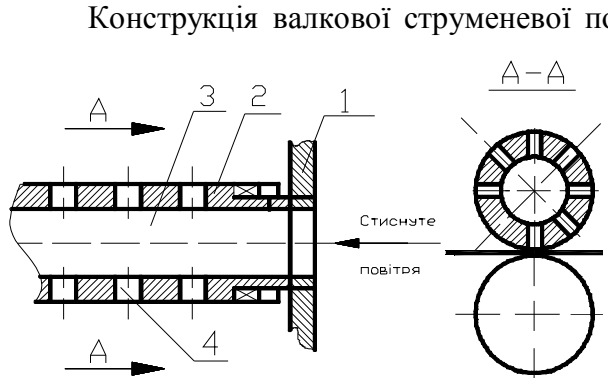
Конструкція валкової подачі у вигляді циліндричного барабана з радіальними струменевими отворами-соплами
